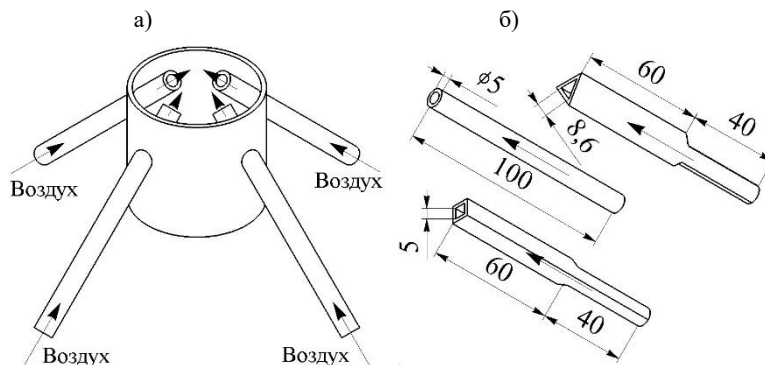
Общий вид конструкции для сопловой подачи воздуха в вертикальный диффузор (а) и геометрические размеры подающих трубок с разными формами поперечного сечения (б)
